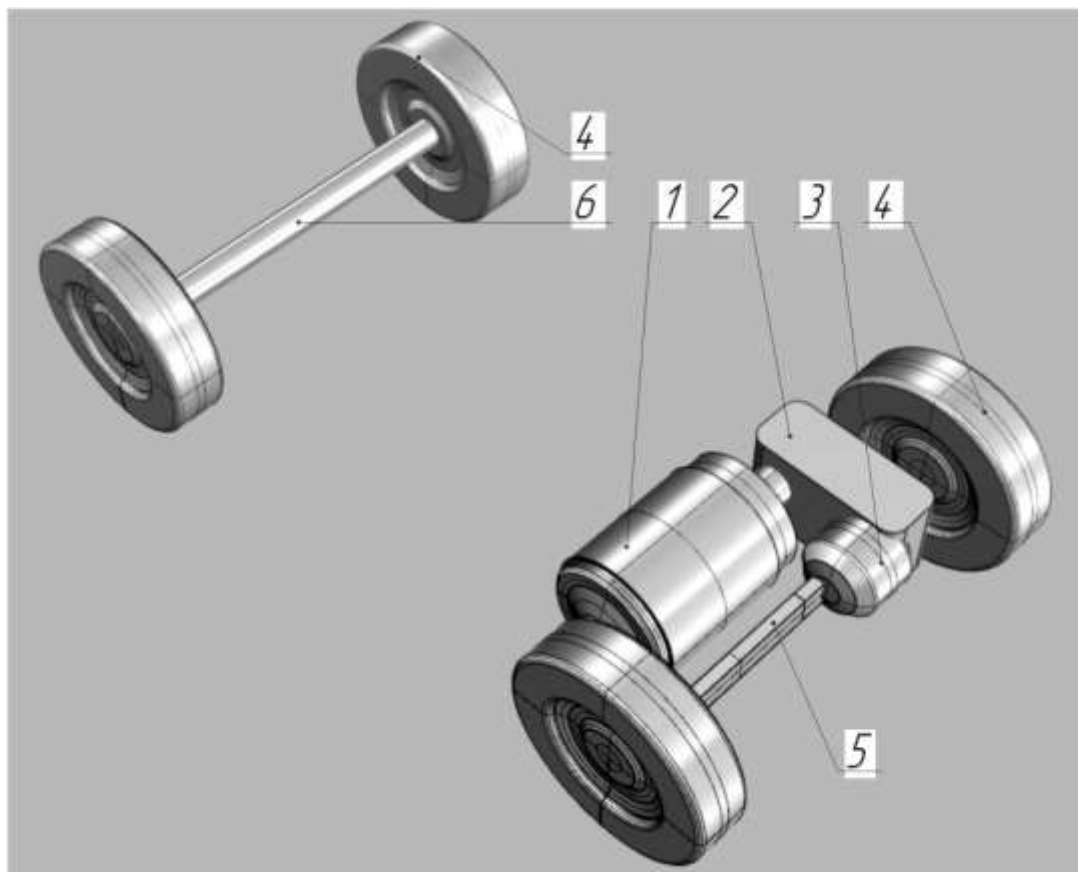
Общий вид привода на задние колеса с двигателем, установленным параллельно оси: 1 – электрический двигатель, 2 – редуктор, 3 – главная передача с дифференциалом, 4 – колесо, 5 – передняя управляемая ось, 6 – задняя ведущая ось
